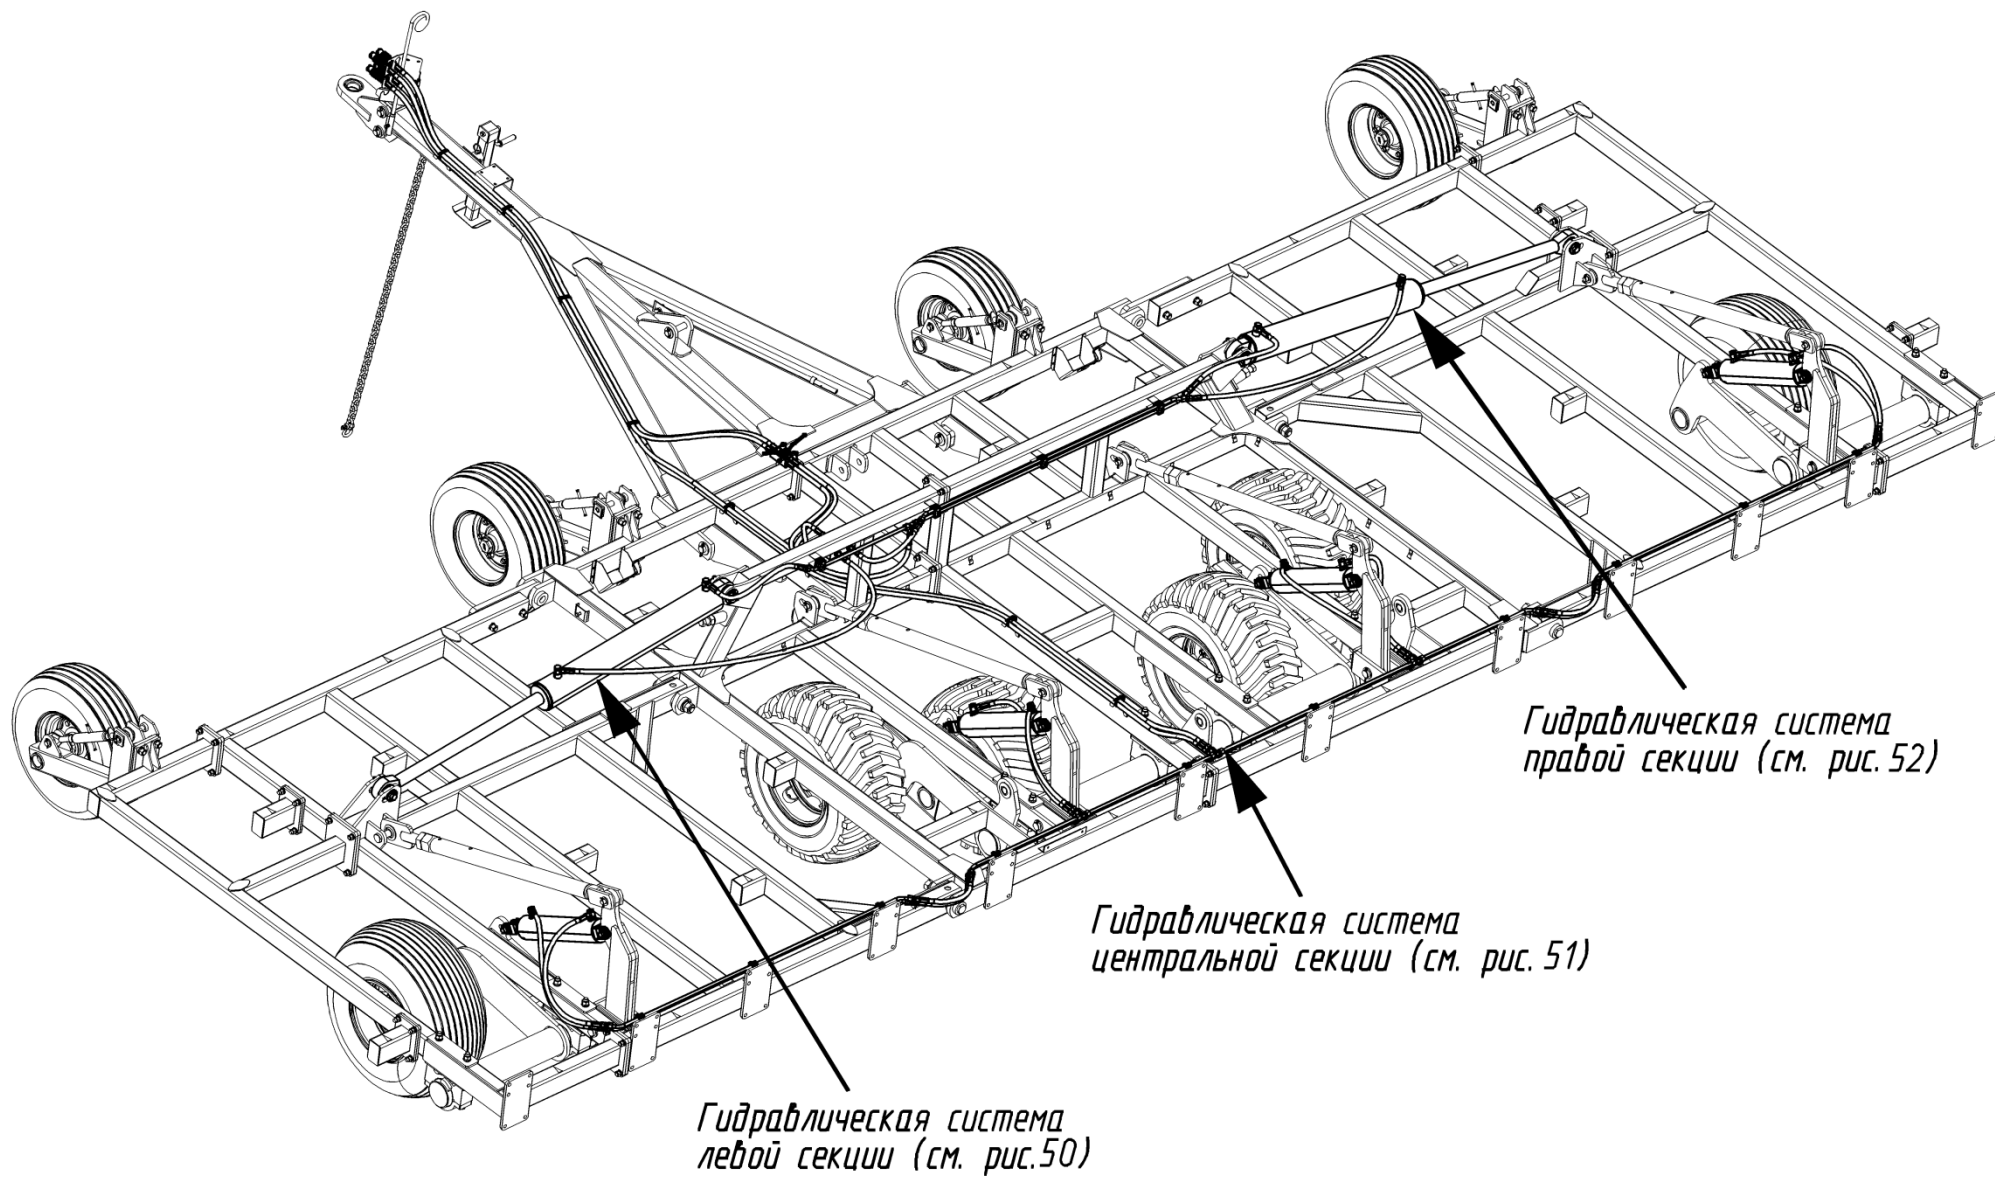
Установка гидрооборудования К-102.12.000А
